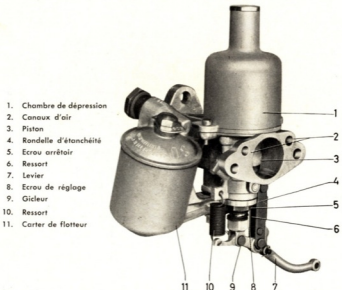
Carburateur arrière vu du côté du carter de flotteur.
